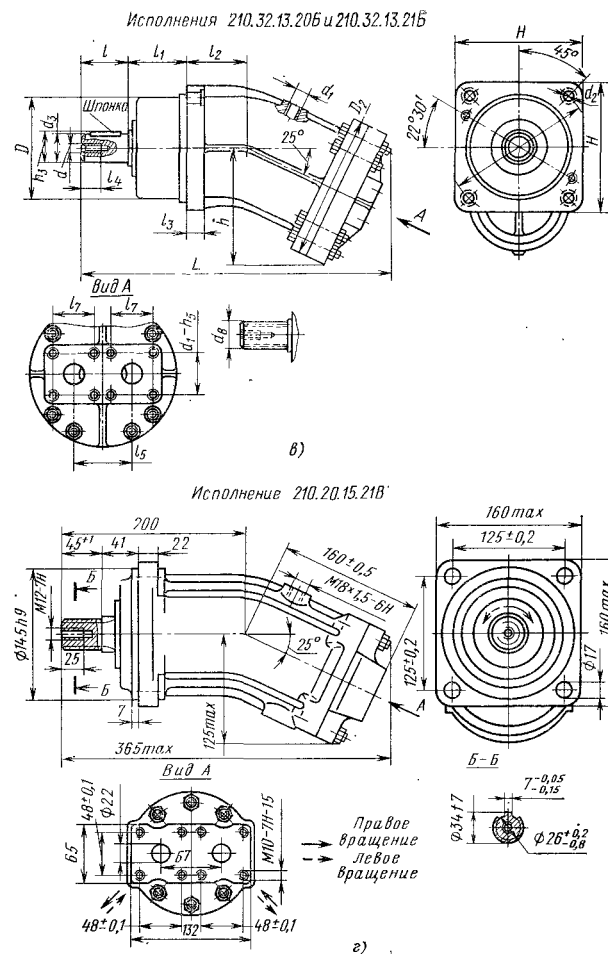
Габаритные и присоединительные размеры гидромашин типа 210
